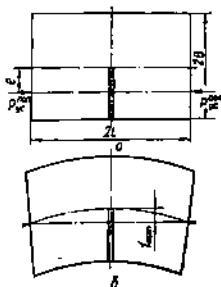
Деформации изгиба от сварки *встык* пластин различной ширины
